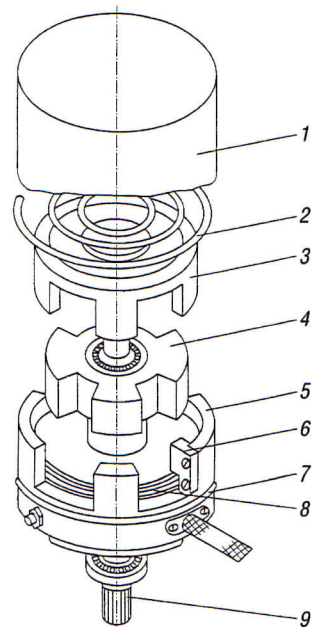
Схема устройства поворотного магнита: 1 — колпак; 2 — пружина; 3 — якорь; 4 — магнитопровод; 5 — корпус; 6 — упор; 7 — кольцо; 8 — катушка; 9 — вал
